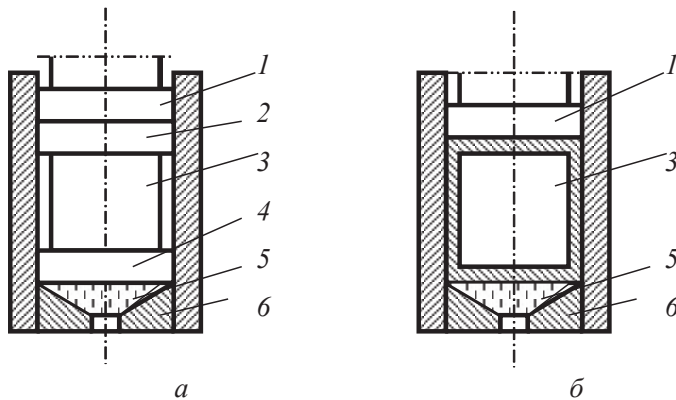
Сборка инструментальной оснастки для прессования со стальными шайбами (а) и их распрессовка (б):
